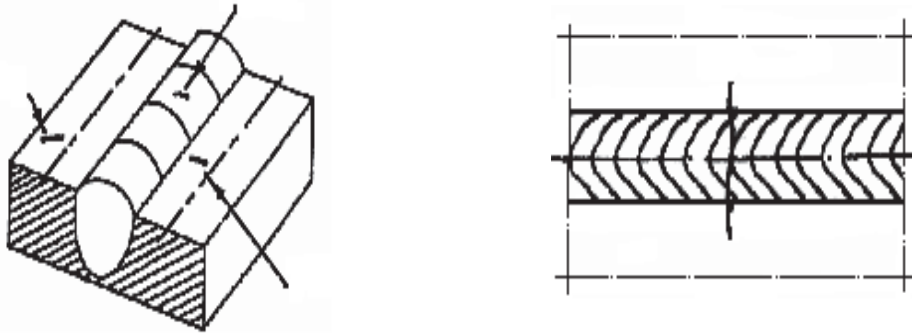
Схематическое изображение поперечной трещины сварного соединения
